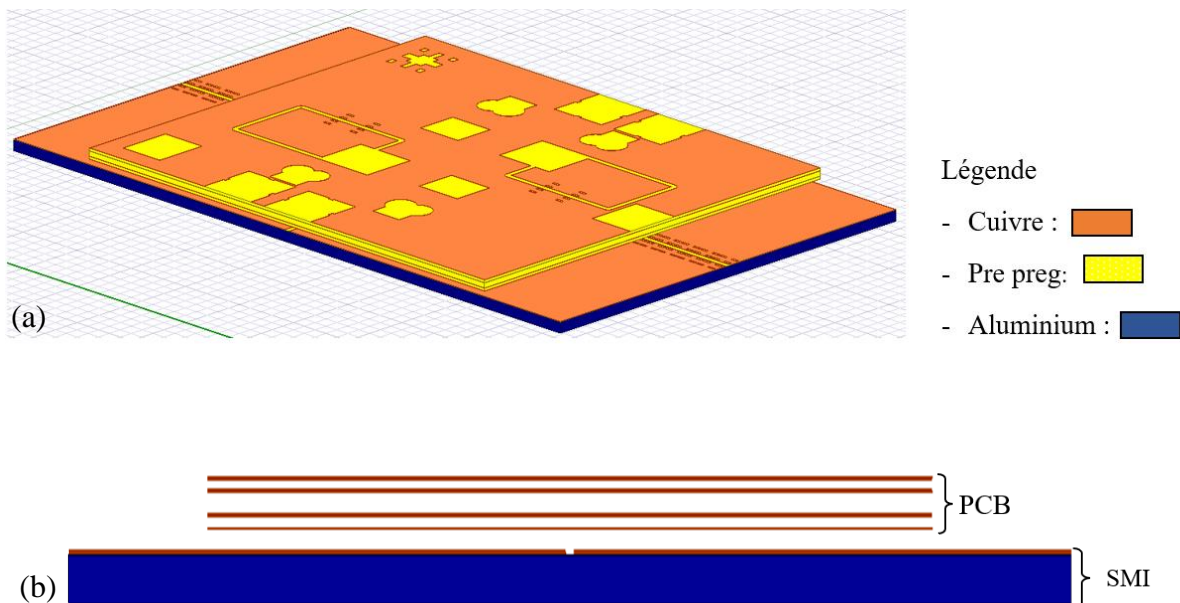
Géométrie du module PP_PCBSMI dans Ansys Q3D extractor (a) Vue isométrique (b) Coupe transversale
